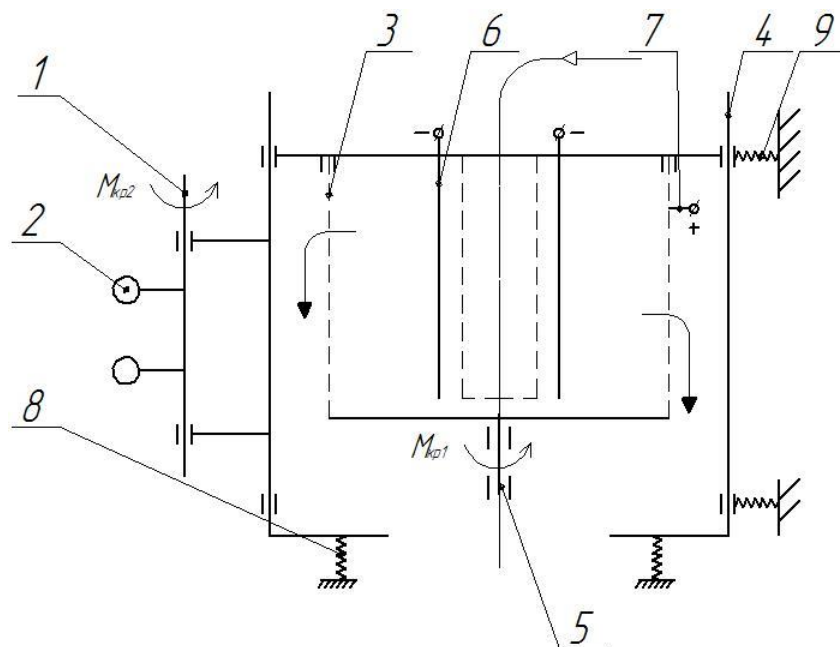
Принципова схема розробленої машини: 1 - приводний вал вібробуджувача, 2 - дебаланс, 3 - контейнер, 4 - зовнішній корпус або віброплатформа, 5 - приводний вал центрифуги, 6, 7 - електроди, 8 - пружна опора, 9 - пружний елемент віброплатформи
